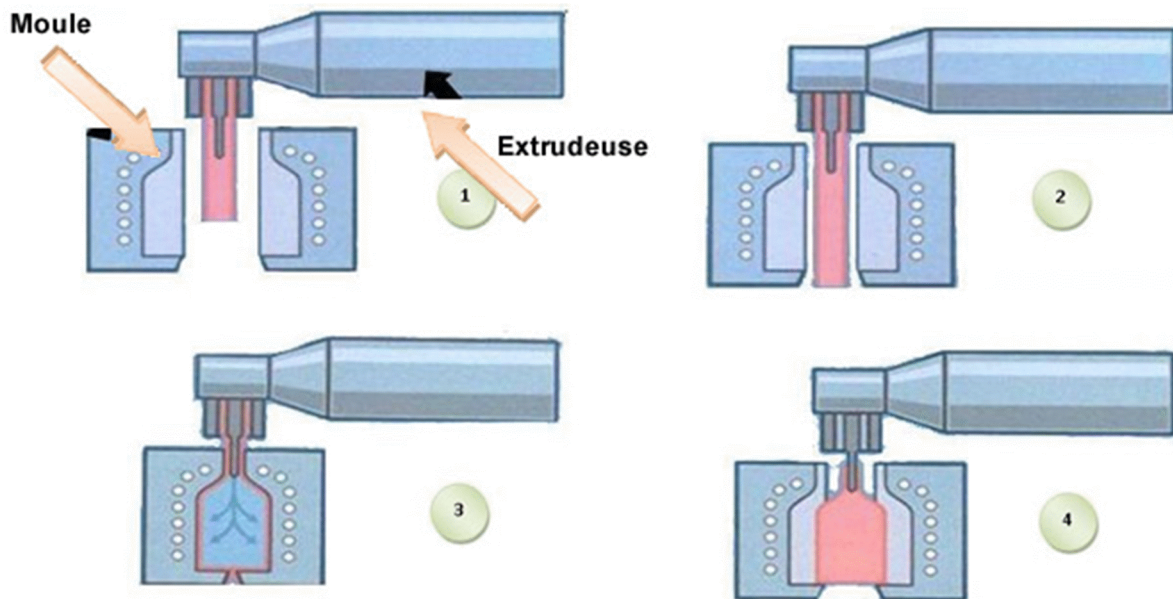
Procédé de mise en œuvre par extrusion soufflage
